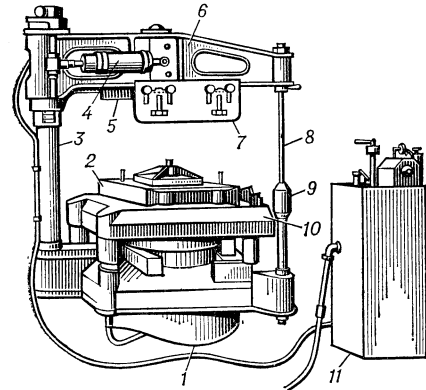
Формовочная машина: 1 — станина; 2 — модельная плита; 3 — колонна прессовой траверсы; 4 — цилиндр поворота траверсы; 5 — прессовая колодка; 6 — прессовая траверса; 7 — сталкиватель готовых полуформ на конвейер; 8 — стойка (дополнительная опора) прессовой траверсы; 9 — замок стойки траверсы; 10 — протяжная рама; 11 — колонка управления.
